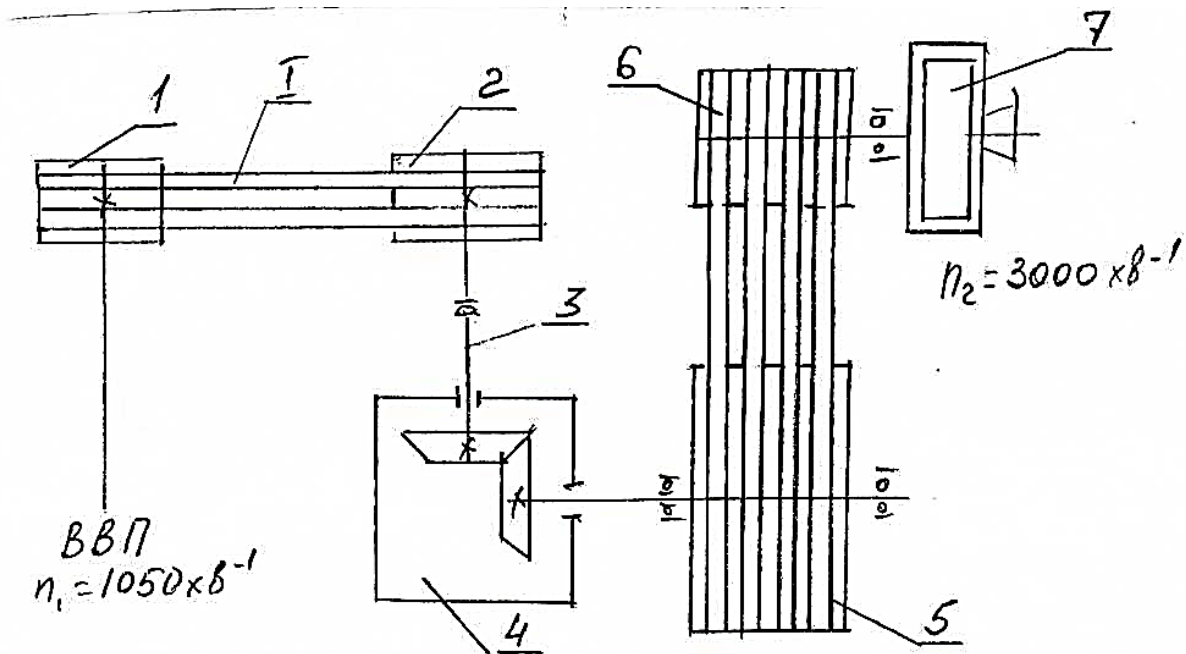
Схема приводу вентилятора: 1- ведучий шків; 2 - відомий шків; 3 – проміжний вал; 4 – редуктор; 5 – ведучий шків; 6 – відомий шків; 7 – вентилятор
